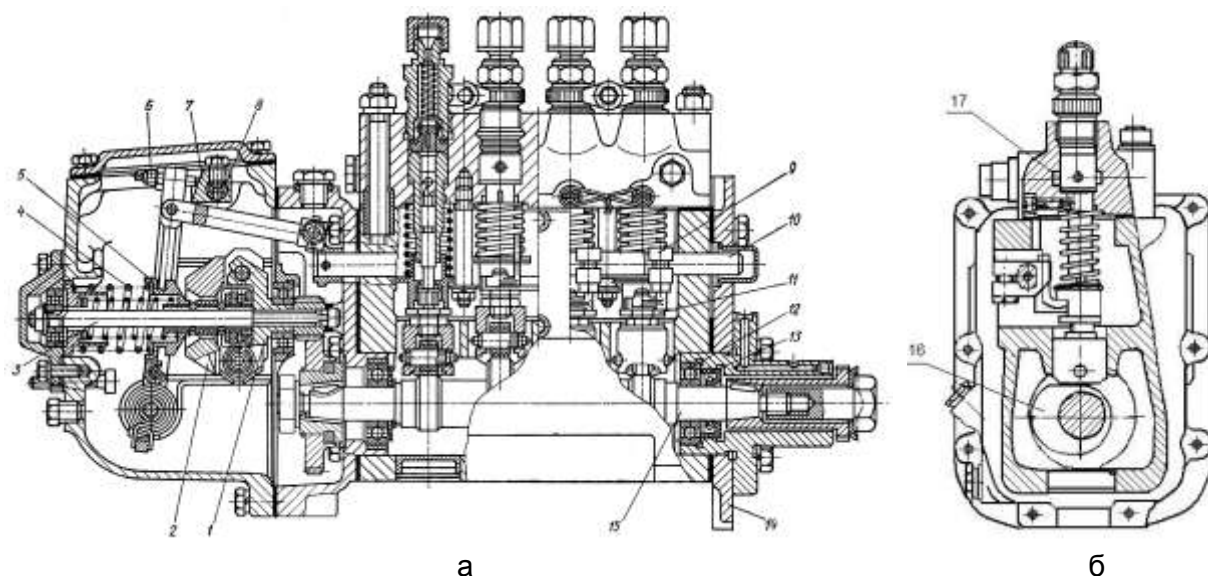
Топливный насос серии ТН с П-образным топливоподающим каналом головки (а) и одноканальной головкой ТНВД (б): 1 - ступица регулятора; 2 - груз; 3 - валик регулятора; 4 - пружина регулятора; 5 - муфта; 6 - вильчатый рычаг; 7 - призматический упор; 8 - валик обогатителя; 9 - поводок плунжера; 10 - рейка; 11 - толкатель; 12 - подшипник; 13 – уплотнение; 14 - фланец; 15 - кулачковый вал; 16 – несимметричный кулачковый вал; 17 – вариант исполнения головки насоса с одним центральным каналом подвода топлива.
